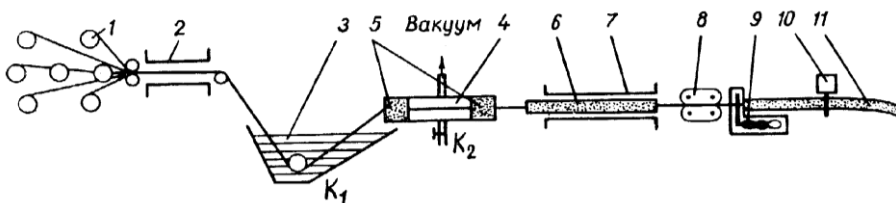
Технологическая схема непрерывной протяжки стеклопластикового стержня с повышенными электроизоляционными свойствами при использовании вакуумной камеры:
